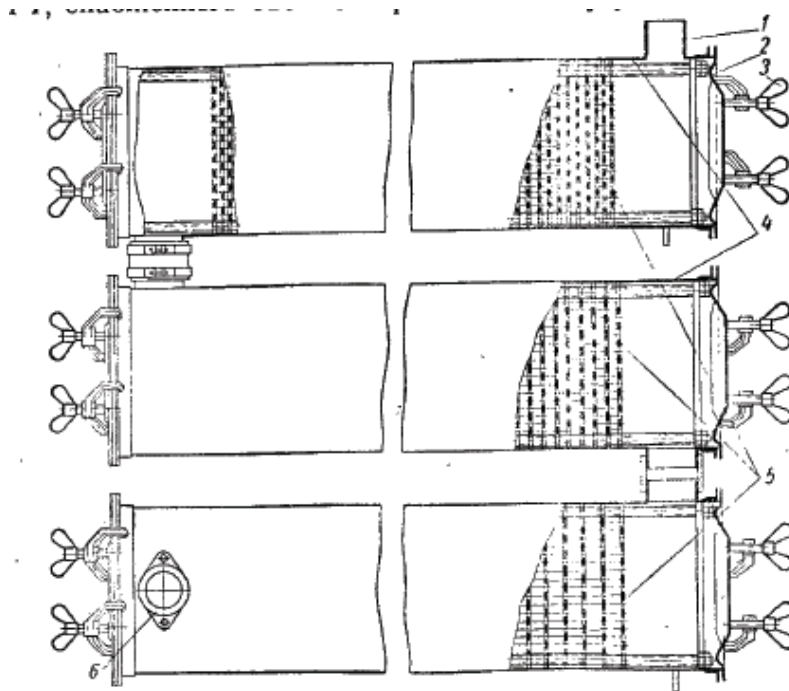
Батарея грубих очищувачів-охолоджувачів з перфорованими пластинами: 1 – вихідний патрубок; 2-кришка очищувача, 3-затяжний гвинт кришки, 4 - корпус очищувача, 5 – перфЗоровані пластини, 6 - вхідний патрубок
